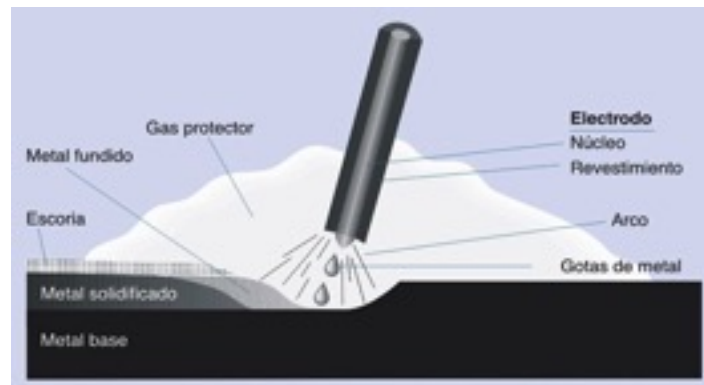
Proceso de soldadura por arco eléctrico
